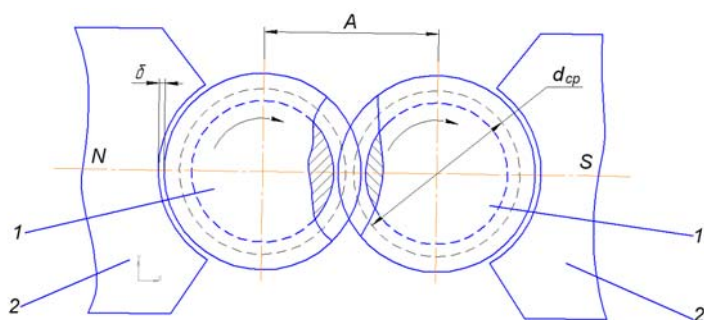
Схема установки для МАО винтовых поверхностей
